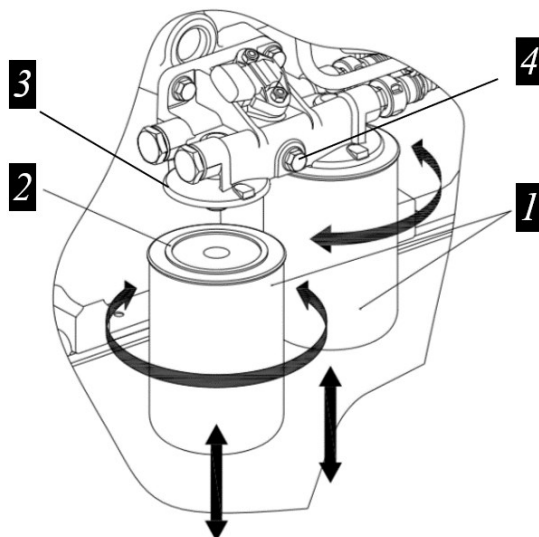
Фильтры тонкой очистки топлива ЯМЗ-536
